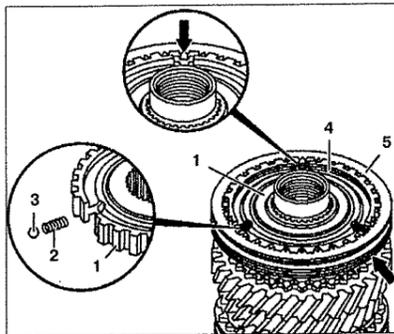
Разборка и сборка шестерни 5-й передачи:
